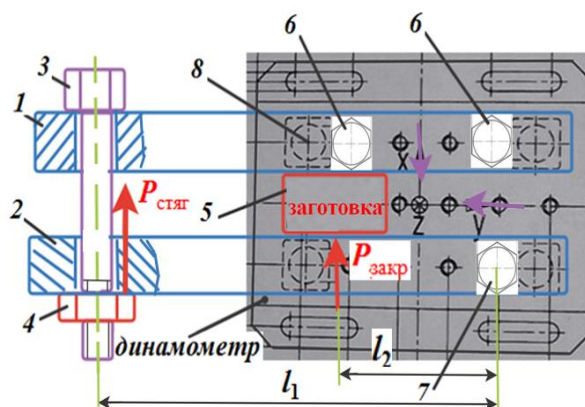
Схема закрепления небольшого образца на динамометре Kistler для фрезерования концевой фрезой
